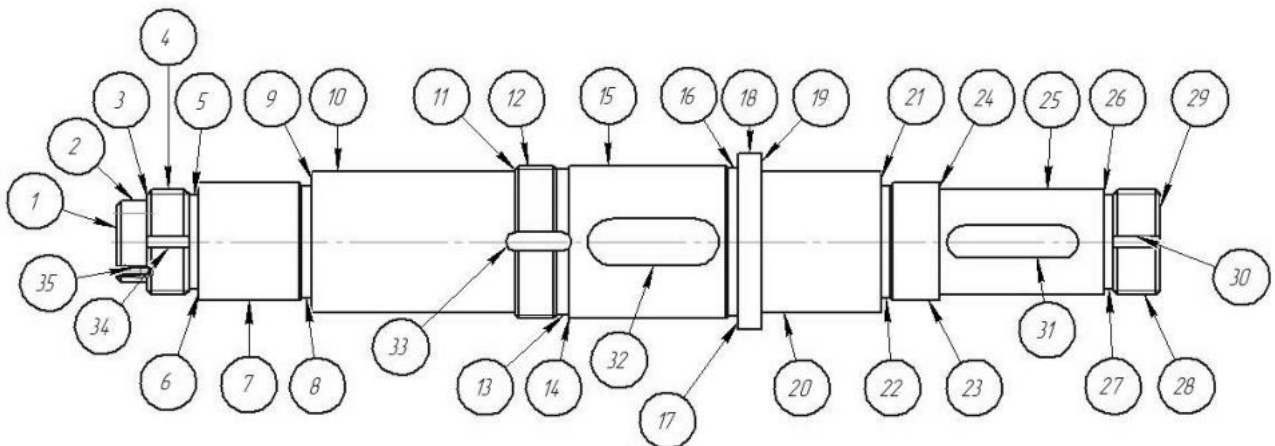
Ескіз деталі із нумерацією основних поверхонь
